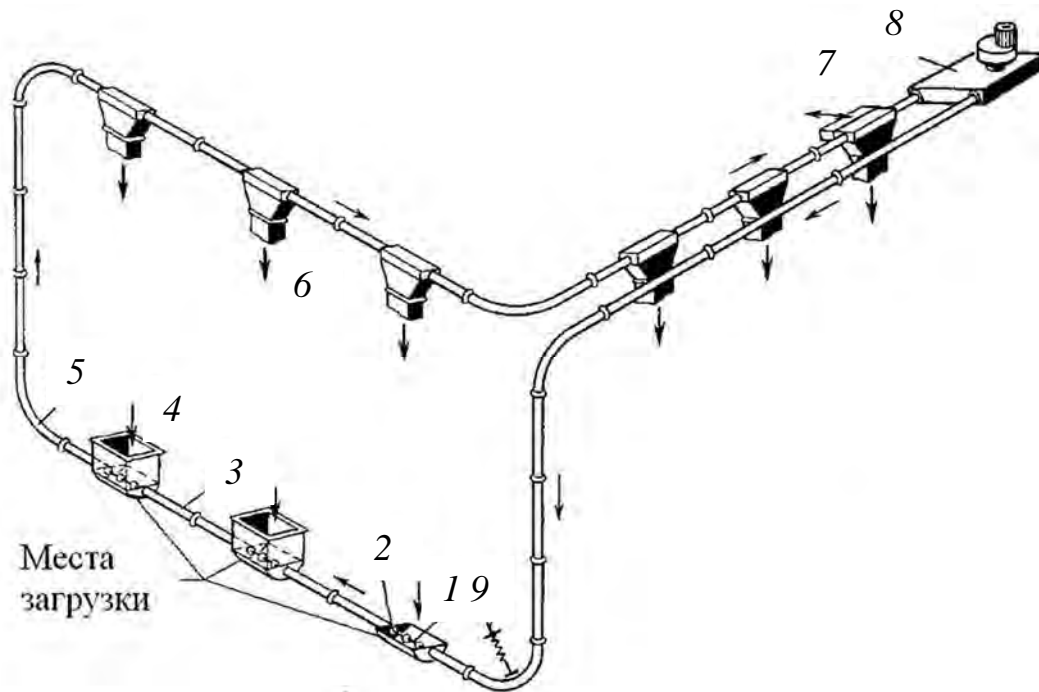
Схема трубчатого скребкового конвейера: 1 – цепь; 2 – скребки; 3 – труба; 4 – загрузочное устройство; 5 – поворотные устройства; 6 – разгрузочный бункер; 7 – очистное устройство; 8 – привод; 9 – натяжное устройство
